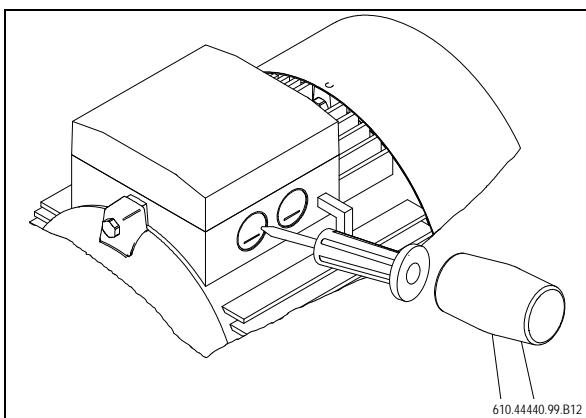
Öffnungen Klemmenkasten ausschlagen
